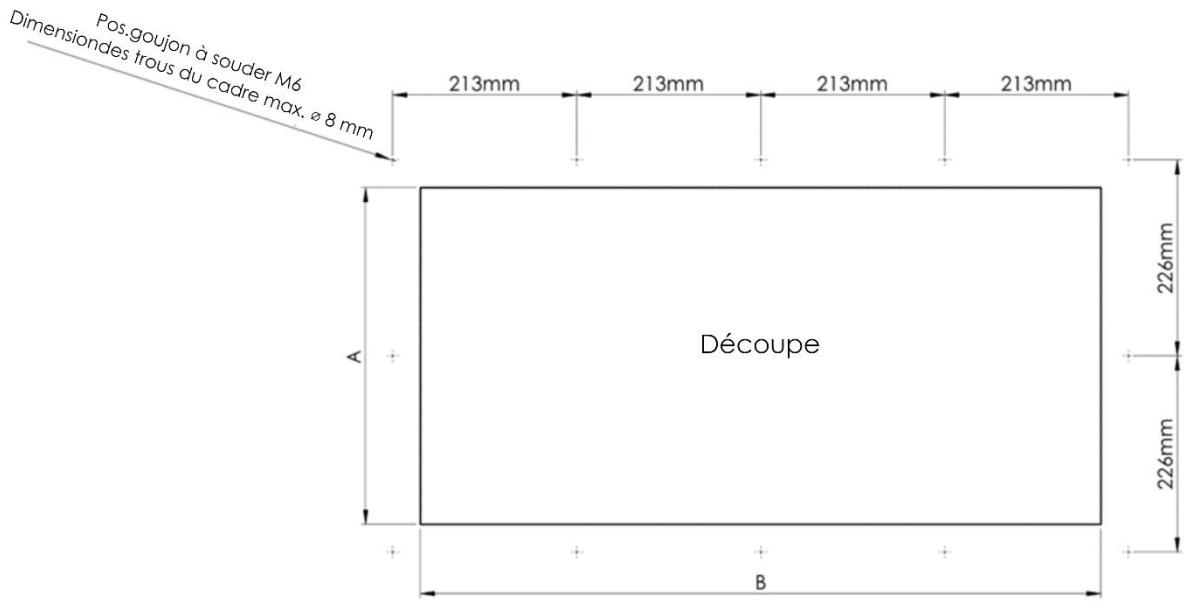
Découpe pour cadre de montage MS-I-20 EG
